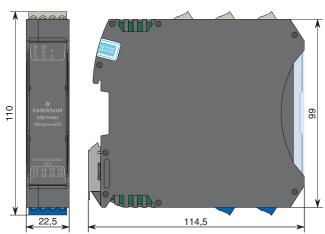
Габаритные размеры барьера в корпусе шириной 22,5 мм с разъемами с винтовыми клеммниками
